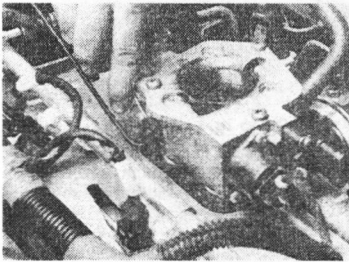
Используйте маленькую отвертку чтобы вытащить вакуумную трубку датчика АДК из задней стороны корпуса дросселя
